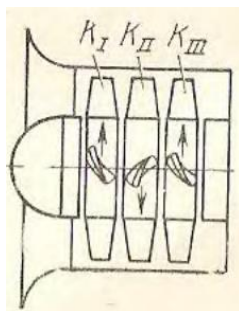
Тріступінчастий вентилятор зустрічного обертання
